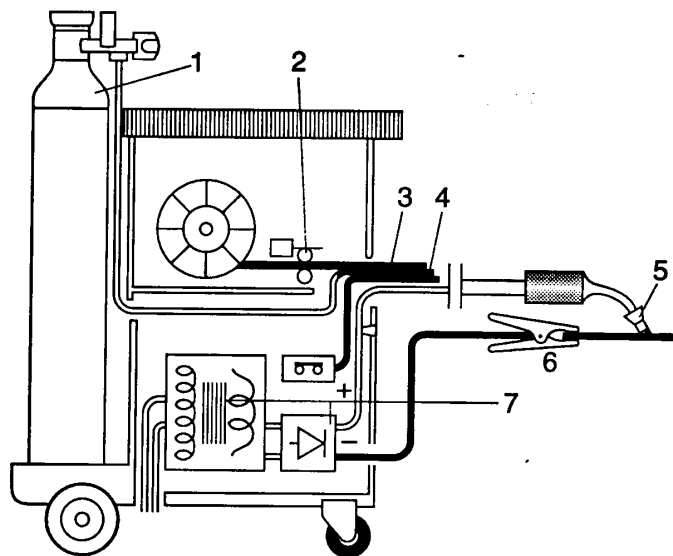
Зварювальний напіваавтомат для зварювання в захисному газі:
